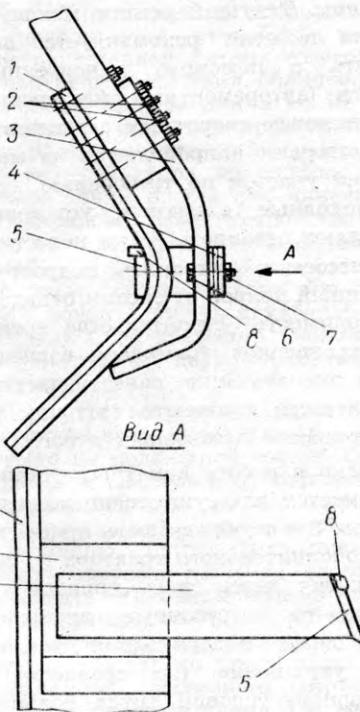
Схема установки дополнительного приспособления на машине ЛП-30Б:
